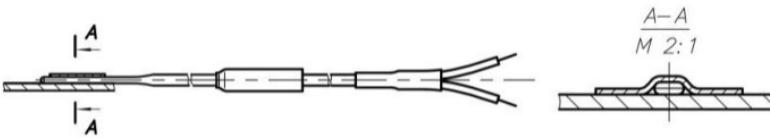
Способ монтажа датчика на основе КТМС на плоскую поверхность с помощью сварки
